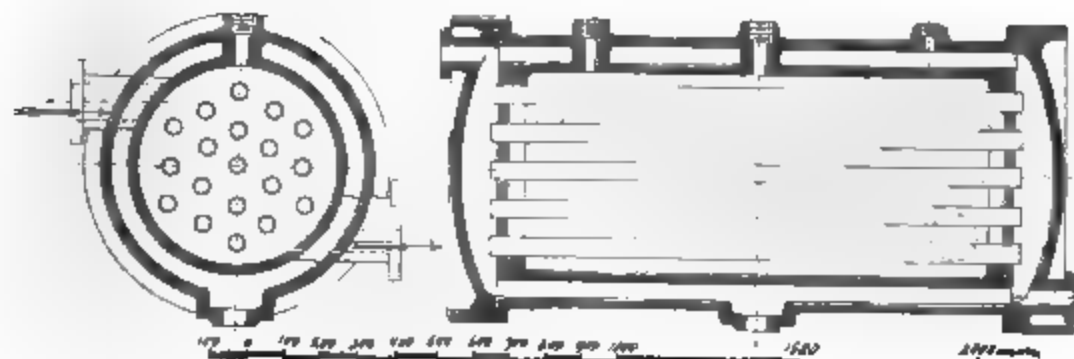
1566. Receiver für stehende Wasserwerksmaschine.
